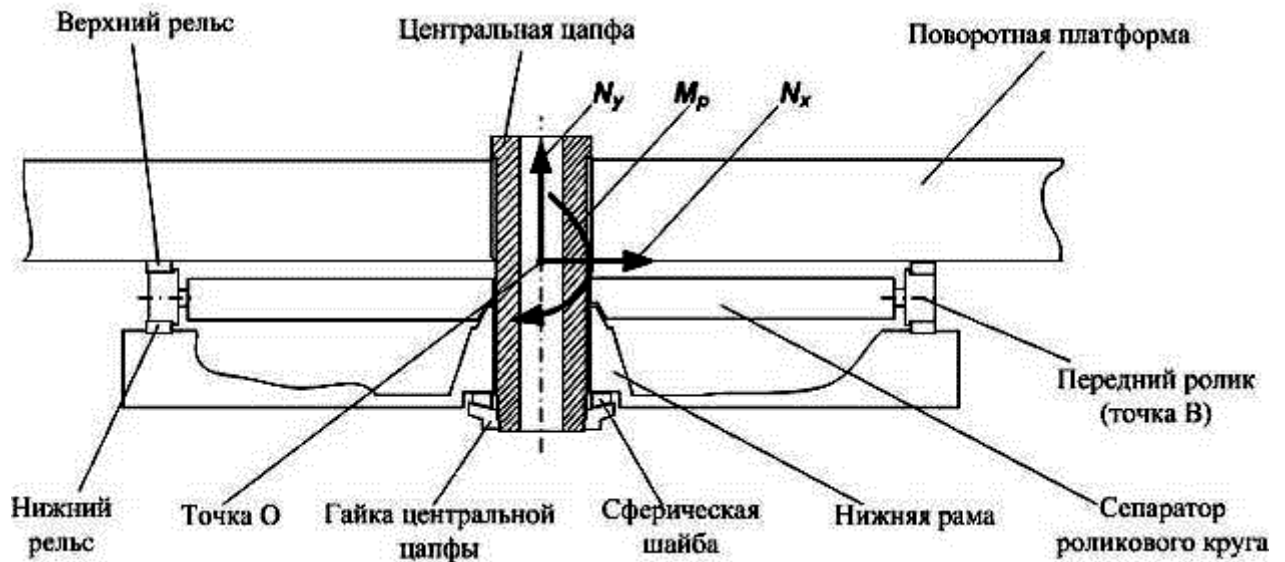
Схема общей конструкции опорно-поворотного устройства и расположения реакций связей
